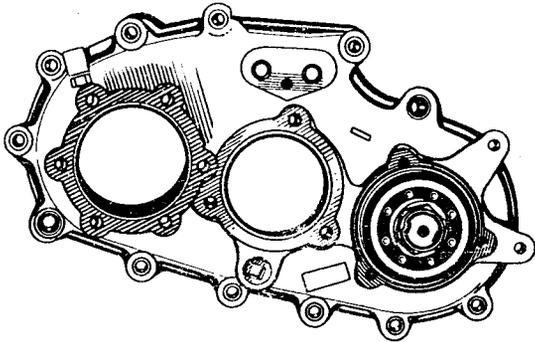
Vorderachsantriebswelle, im Gehäusedeckel eingebaut
